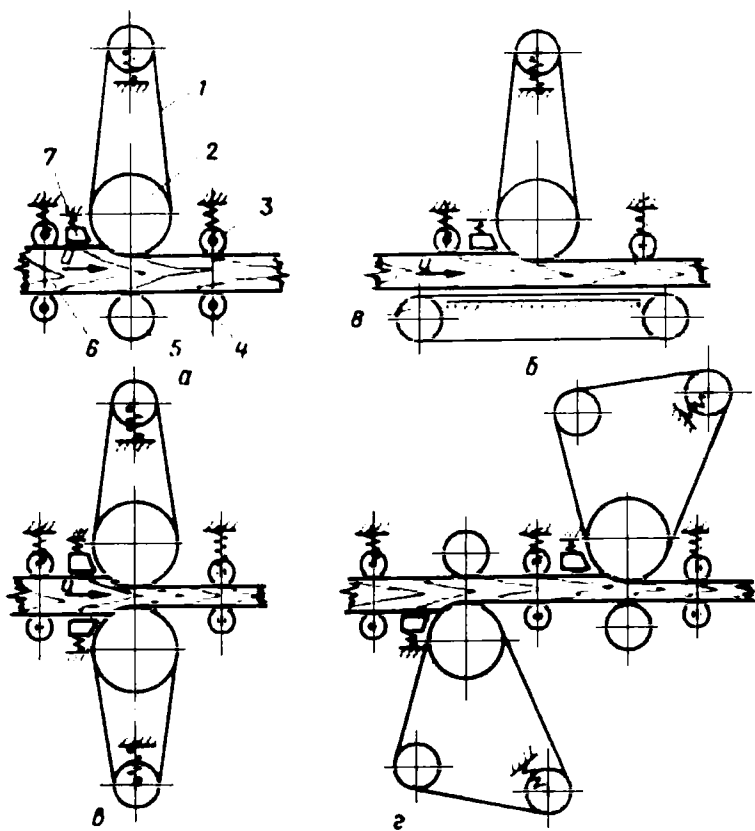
Принципиальные схемы широколенточных шлифовальных станков: а, б — для одностороннего; в, г — двустороннего шлифования; 1 — шлифовальная лента; 2 — контактный валец; 3 — прижимный ролик; 4 — подающий ролик; 5 — контрольный ролик; 6 — лист фанеры (плита); 7 — опорная балка; 8 — подающий конвейер
